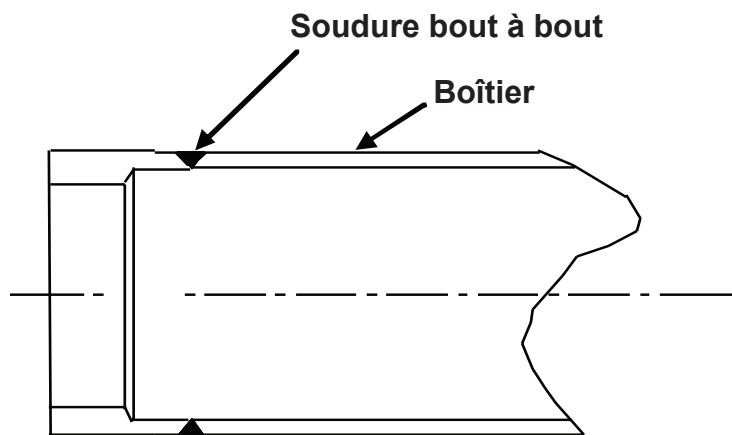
Patin d'entraînement à épaulement, Soudure bout à bout externe
